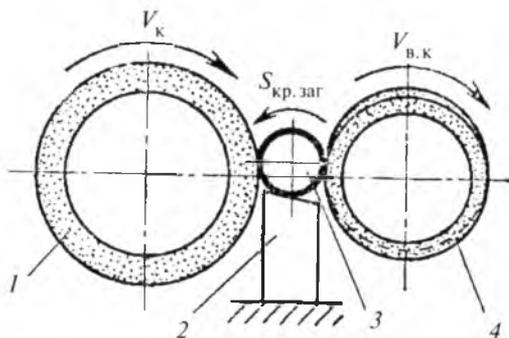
Схема обработки заготовки на бесцентрово-шлифовальных станках:
